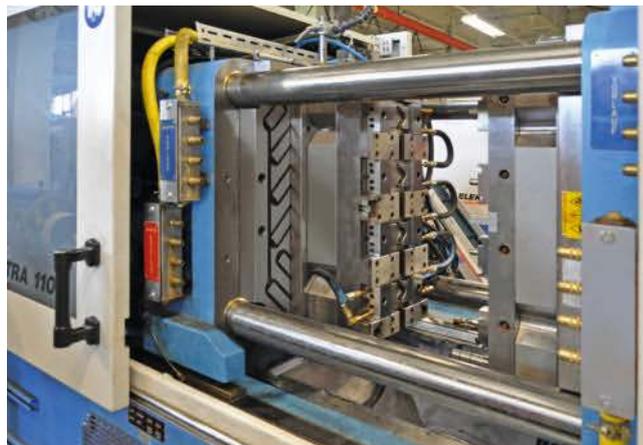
Mtec-Magnetspannplatte im Einsatz auf einer horizontalen Ferromatik-Spritzgießmaschine Elektra 110 evolution (Fotos: Hilma-Römheld)
